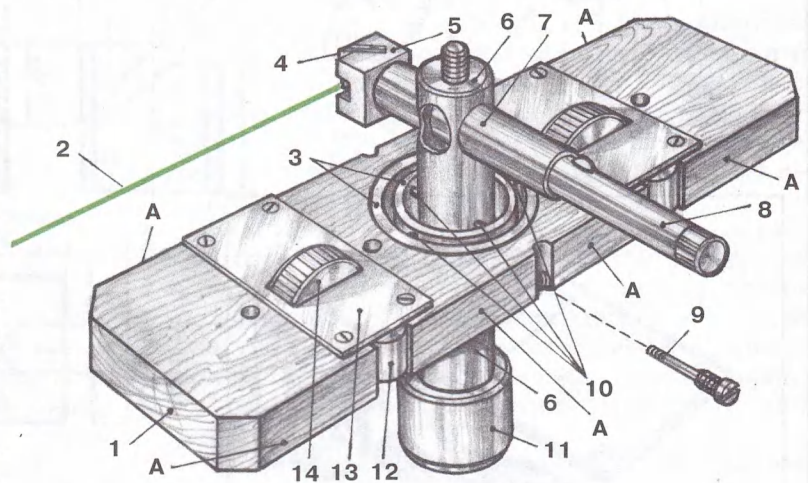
Общий вид устройства: А — базовые поверхности; 1 — платформа; 2 — луч лазера; 3 — кольца плавающего узла; 4 — зеркало; 5 — корпус отражателя; 6 — центральный стержень плавающего узла; 7 — держатель лазерного генератора; 8 — лазерный генератор (лазерная указка); 9 — стопор; 10 — полуоси; 11 — груз; 12 — сухарь установочный угла (4 шт.); 13 — пластина (4 шт.); 14 — ручка юстировки угла (2 шт.).
